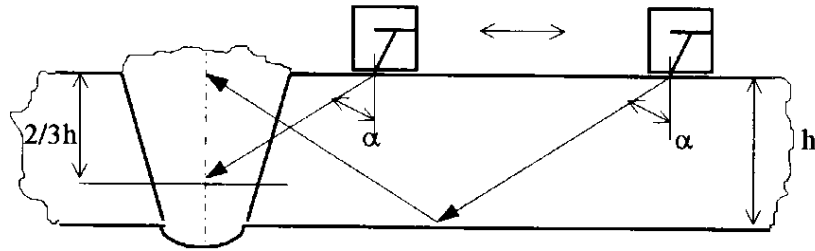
Схема контроля сварного шва малой толщины
